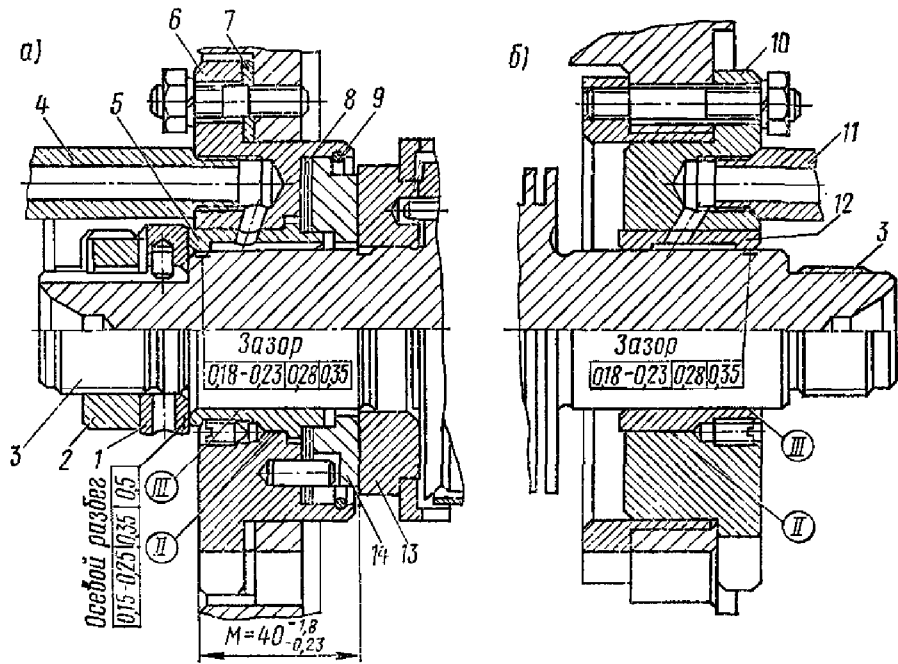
Підшипники турбокомпресорів: а-упорно-опорний; б-опорний, 1-шайба; 2-гайка; 3-вал ротора; 4,11-штуцера; 5-втулка; 6-корпус підшипника; 7-компенсатор; 8-регулювальні пластини; 9-стопорне кільце; 10-корпус; 12-втулка; 13-п'ята; 14-підп'ятник
